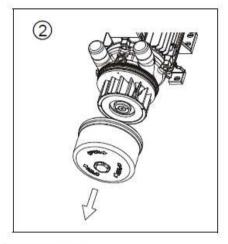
Desmontaje de la carcasa de la bomba de vacio / del compresor Se habrá de efectuar con una llave de boca de anchura  $36 \, [^3/_6]$ "].
